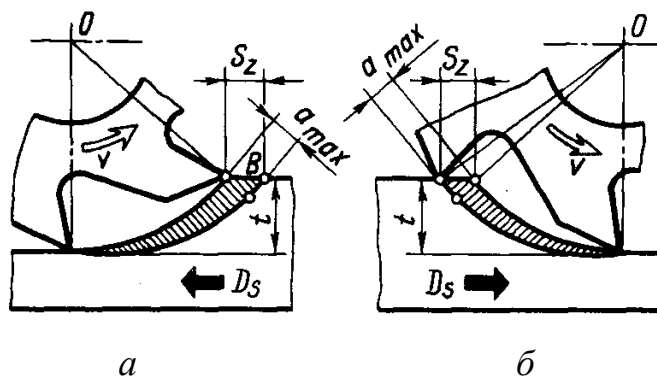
Схемы фрезерования: а – встречное фрезерование; б – попутное
